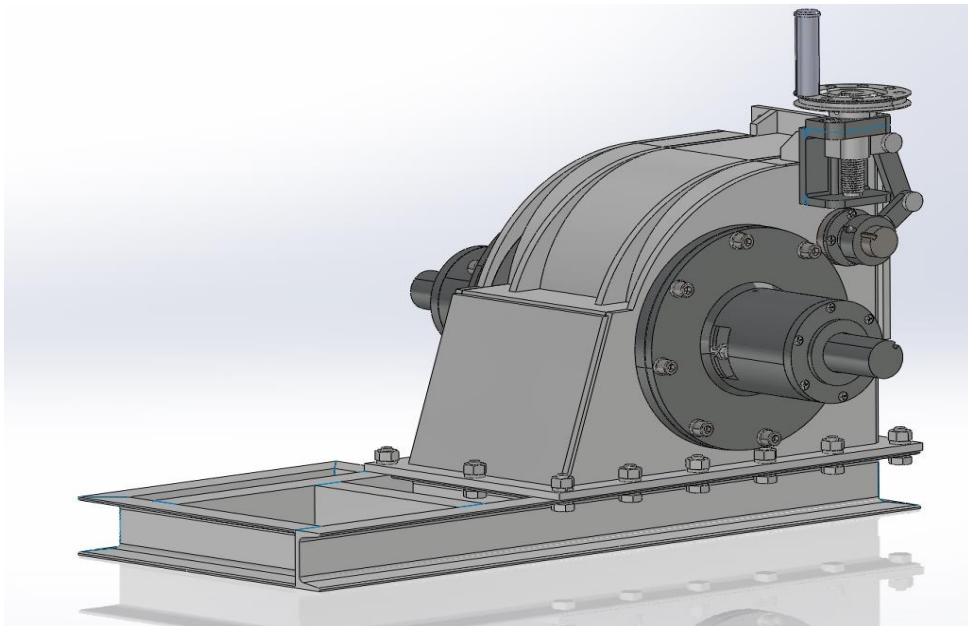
Turbina Michell- Banki diseñada vista lateral trasera izquierda
